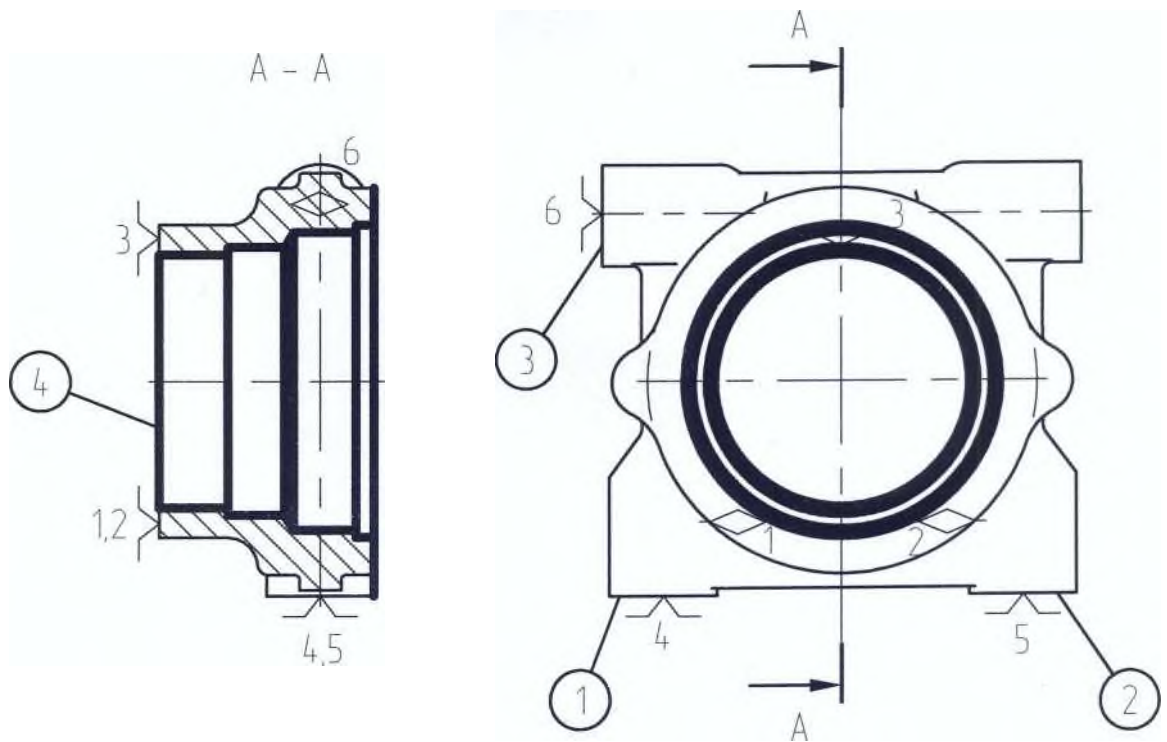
Схема базування заготовки деталі Стойка задня
